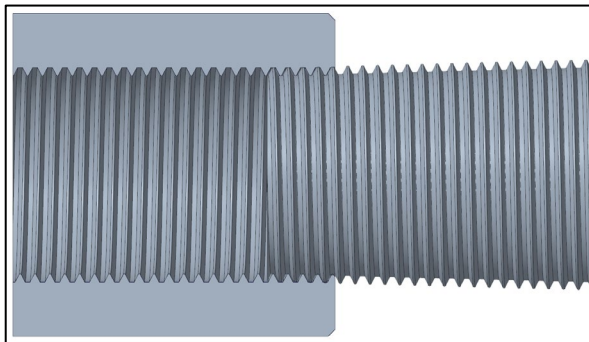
Konisches Außen-, und zylindrisches Innengewinde
